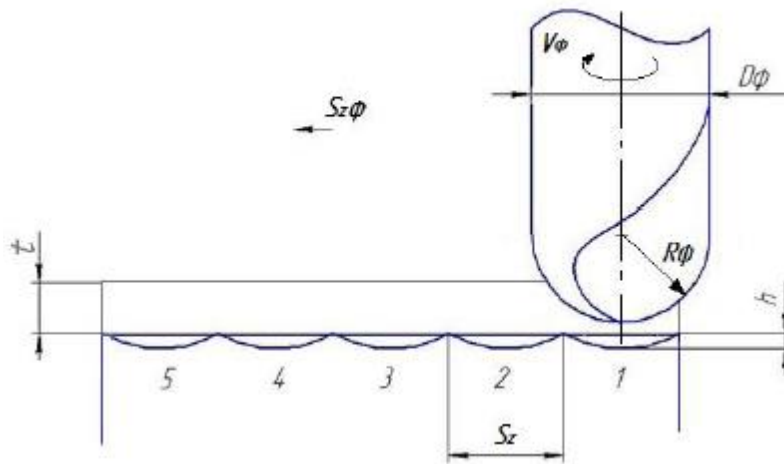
Моделювання формування слідів обробки – гребінців при фрезеруванні кінцевою сферичною фрезою  $\varnothing D\phi$  з подачею  $S_z$
